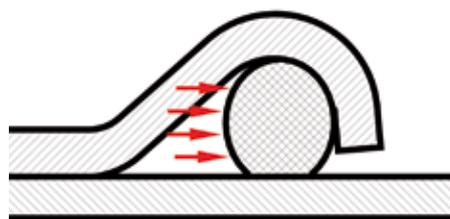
Bei hohen Prüfdrücken kann sich der Dichtring im Fitting verformen
